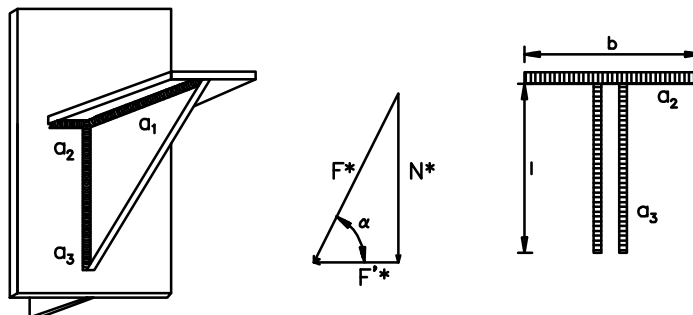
Soldaduras del apoyo rigidizado.
